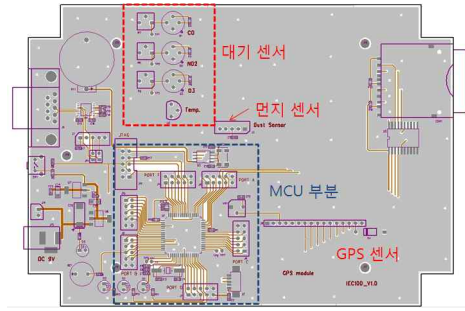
대기오염 모니터링을 위한 RF-Sensor 하드웨어 PCB layout 결과
